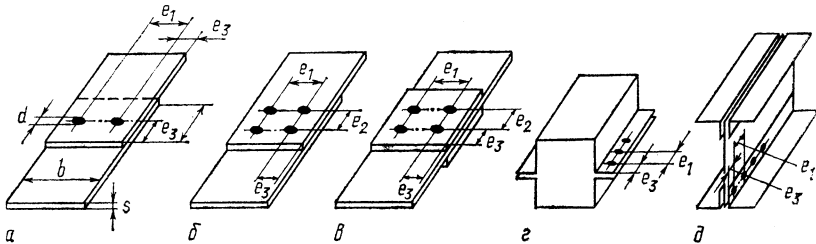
Соединения, получаемые точечной сваркой
